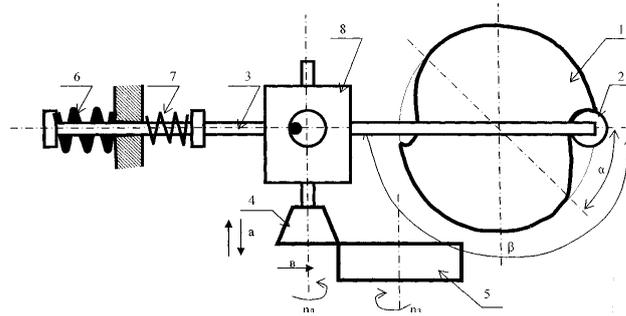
Схема обеспечения врезания и круговой обкатки при зубодолблении заготовки
